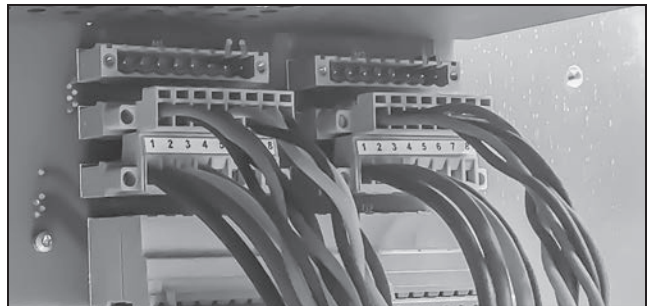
Primer plano de los conectores del tablero posterior del rack de interruptores Vista.
